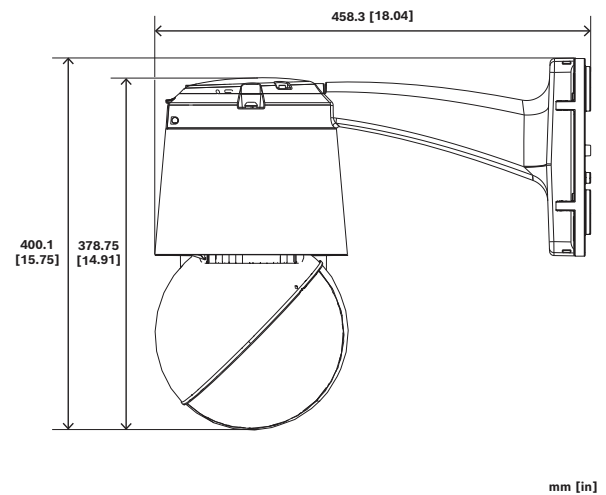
Dimensions en mm de la caméra installée sur NDA-7100-PEN | NDA-7100-PENF avec NDA-PEND-WPLATE (vue latérale)
